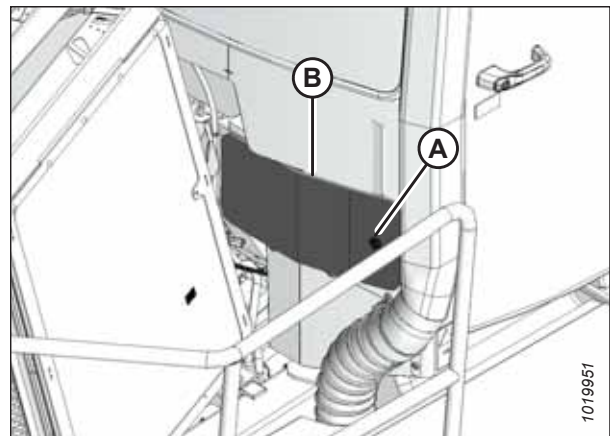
Фильтр на впуске приточного воздуха — крышка
